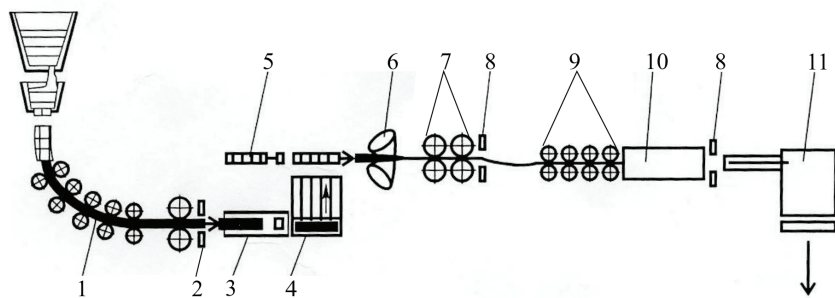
Схема расположения основного оборудования ЛПА конструкции ВНИИ-МЕТМАШа [27]: 1 – МНЛЗ; 2 – делительные ножницы; 3 – индукционный подогреватель; 4 – загрузочная решётка; 5 – толкатель заготовок; 6 – клеть ПВП; 7 – черновая группа клетей продольной прокатки; 8 – летучие ножницы; 9 – чистовая группа клетей; 10 – термоупрочняющая установка; 11 – холодильник
